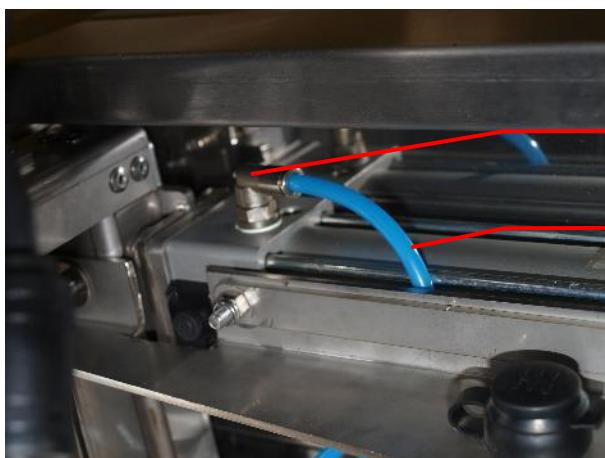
Stecknippel / Schlauch pneumatischer Zylinder vom Türantrieb
